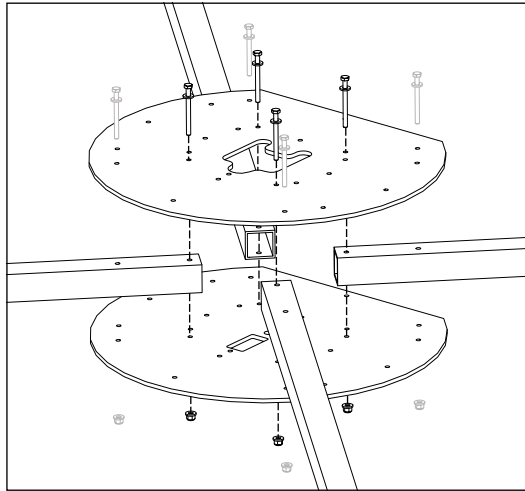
Befestigung der Sensor-Array-Baugruppe
